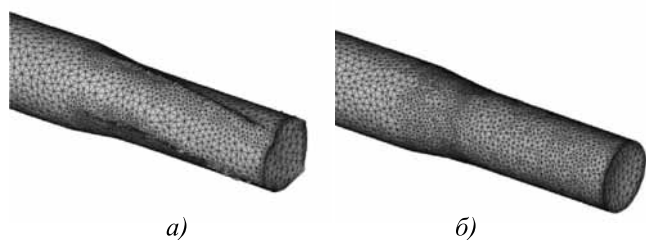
Кованый участок прутка при различной скорости подачи металла при ковке:
